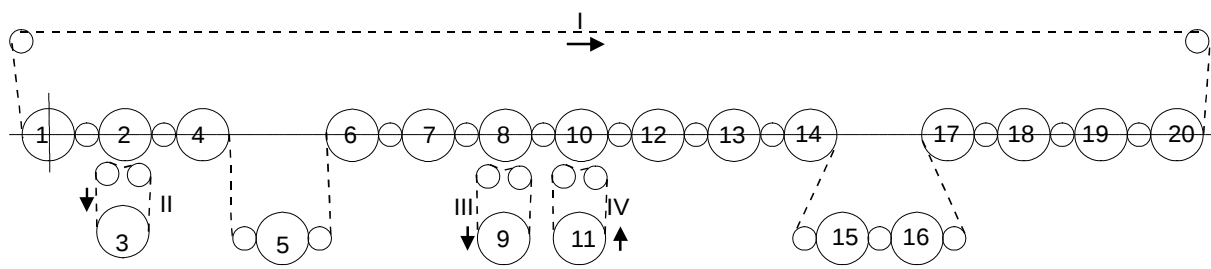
Схема линии сборки двигателей: 1 – загрузочный ротор воспламенительной звезды; 2 – ротор сборки двух элементов; 3 – загрузочный ротор компенсаторов; 4 – ротор контроля комплектности; 5 – загрузочный ротор пороховой шашки; 6 – контрольно-технологический ротор; 7 – ротор лакировки; 8 – ротор сборки двух элементов; 9 – загрузочный ротор; 10 – ротор сборки узла и турбинки; 11 – загрузочный ротор турбинки; 12 – ротор контроля комплектности; 13 – ротор досылки воспламенительной звезды с деталями в турбинку; 14 – ротор контроля; 15 – загрузочный ротор замедлителей; 16 – загрузочный ротор колец; 17 – ротор контроля комплектности; 18 – ротор закатки бортика; 19 – ротор закатки двигателя; 20 – ротор сплошного контроля; I, II, III, IV – транспортные роторы
